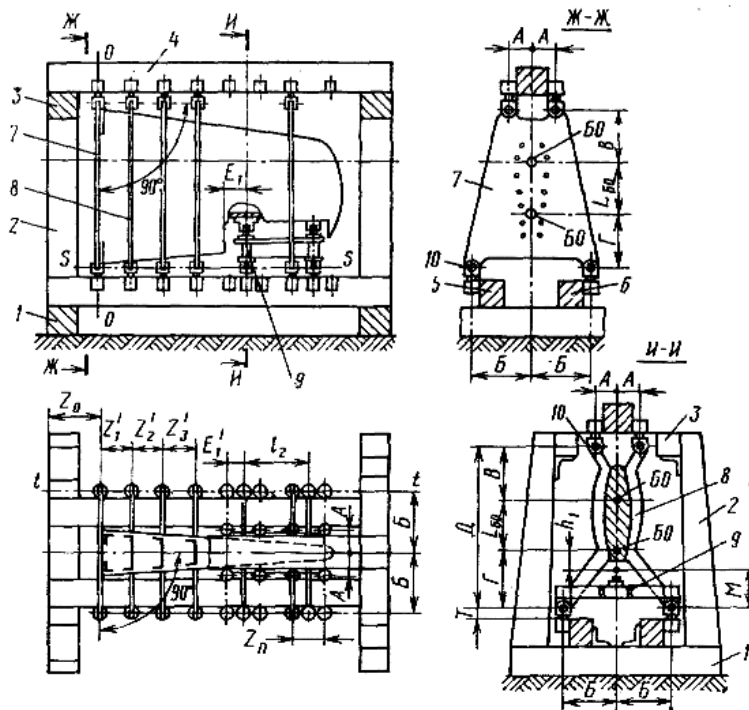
Сборно-разборное приспособление (СРП) для сборки отъемной части крыла:
